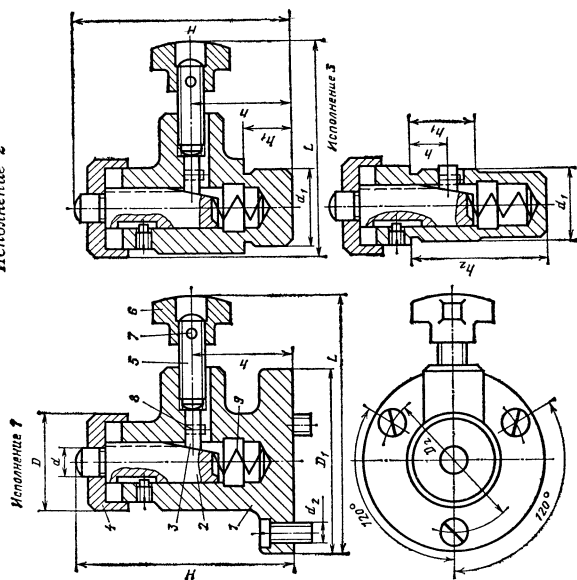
Самоустанавливающиеся опоры по ГОСТ 13159—67*: 1 — корпус; 2 — опорный штырь; 3 — палец; 4 — колышак; 5 — винт (ГОСТ 13428—68*); 6 — рукоятка (ГОСТ 4742—68*); 7 и 8 — цилиндрические штифты; 9 — пружина (ГОСТ 13165—67*)
